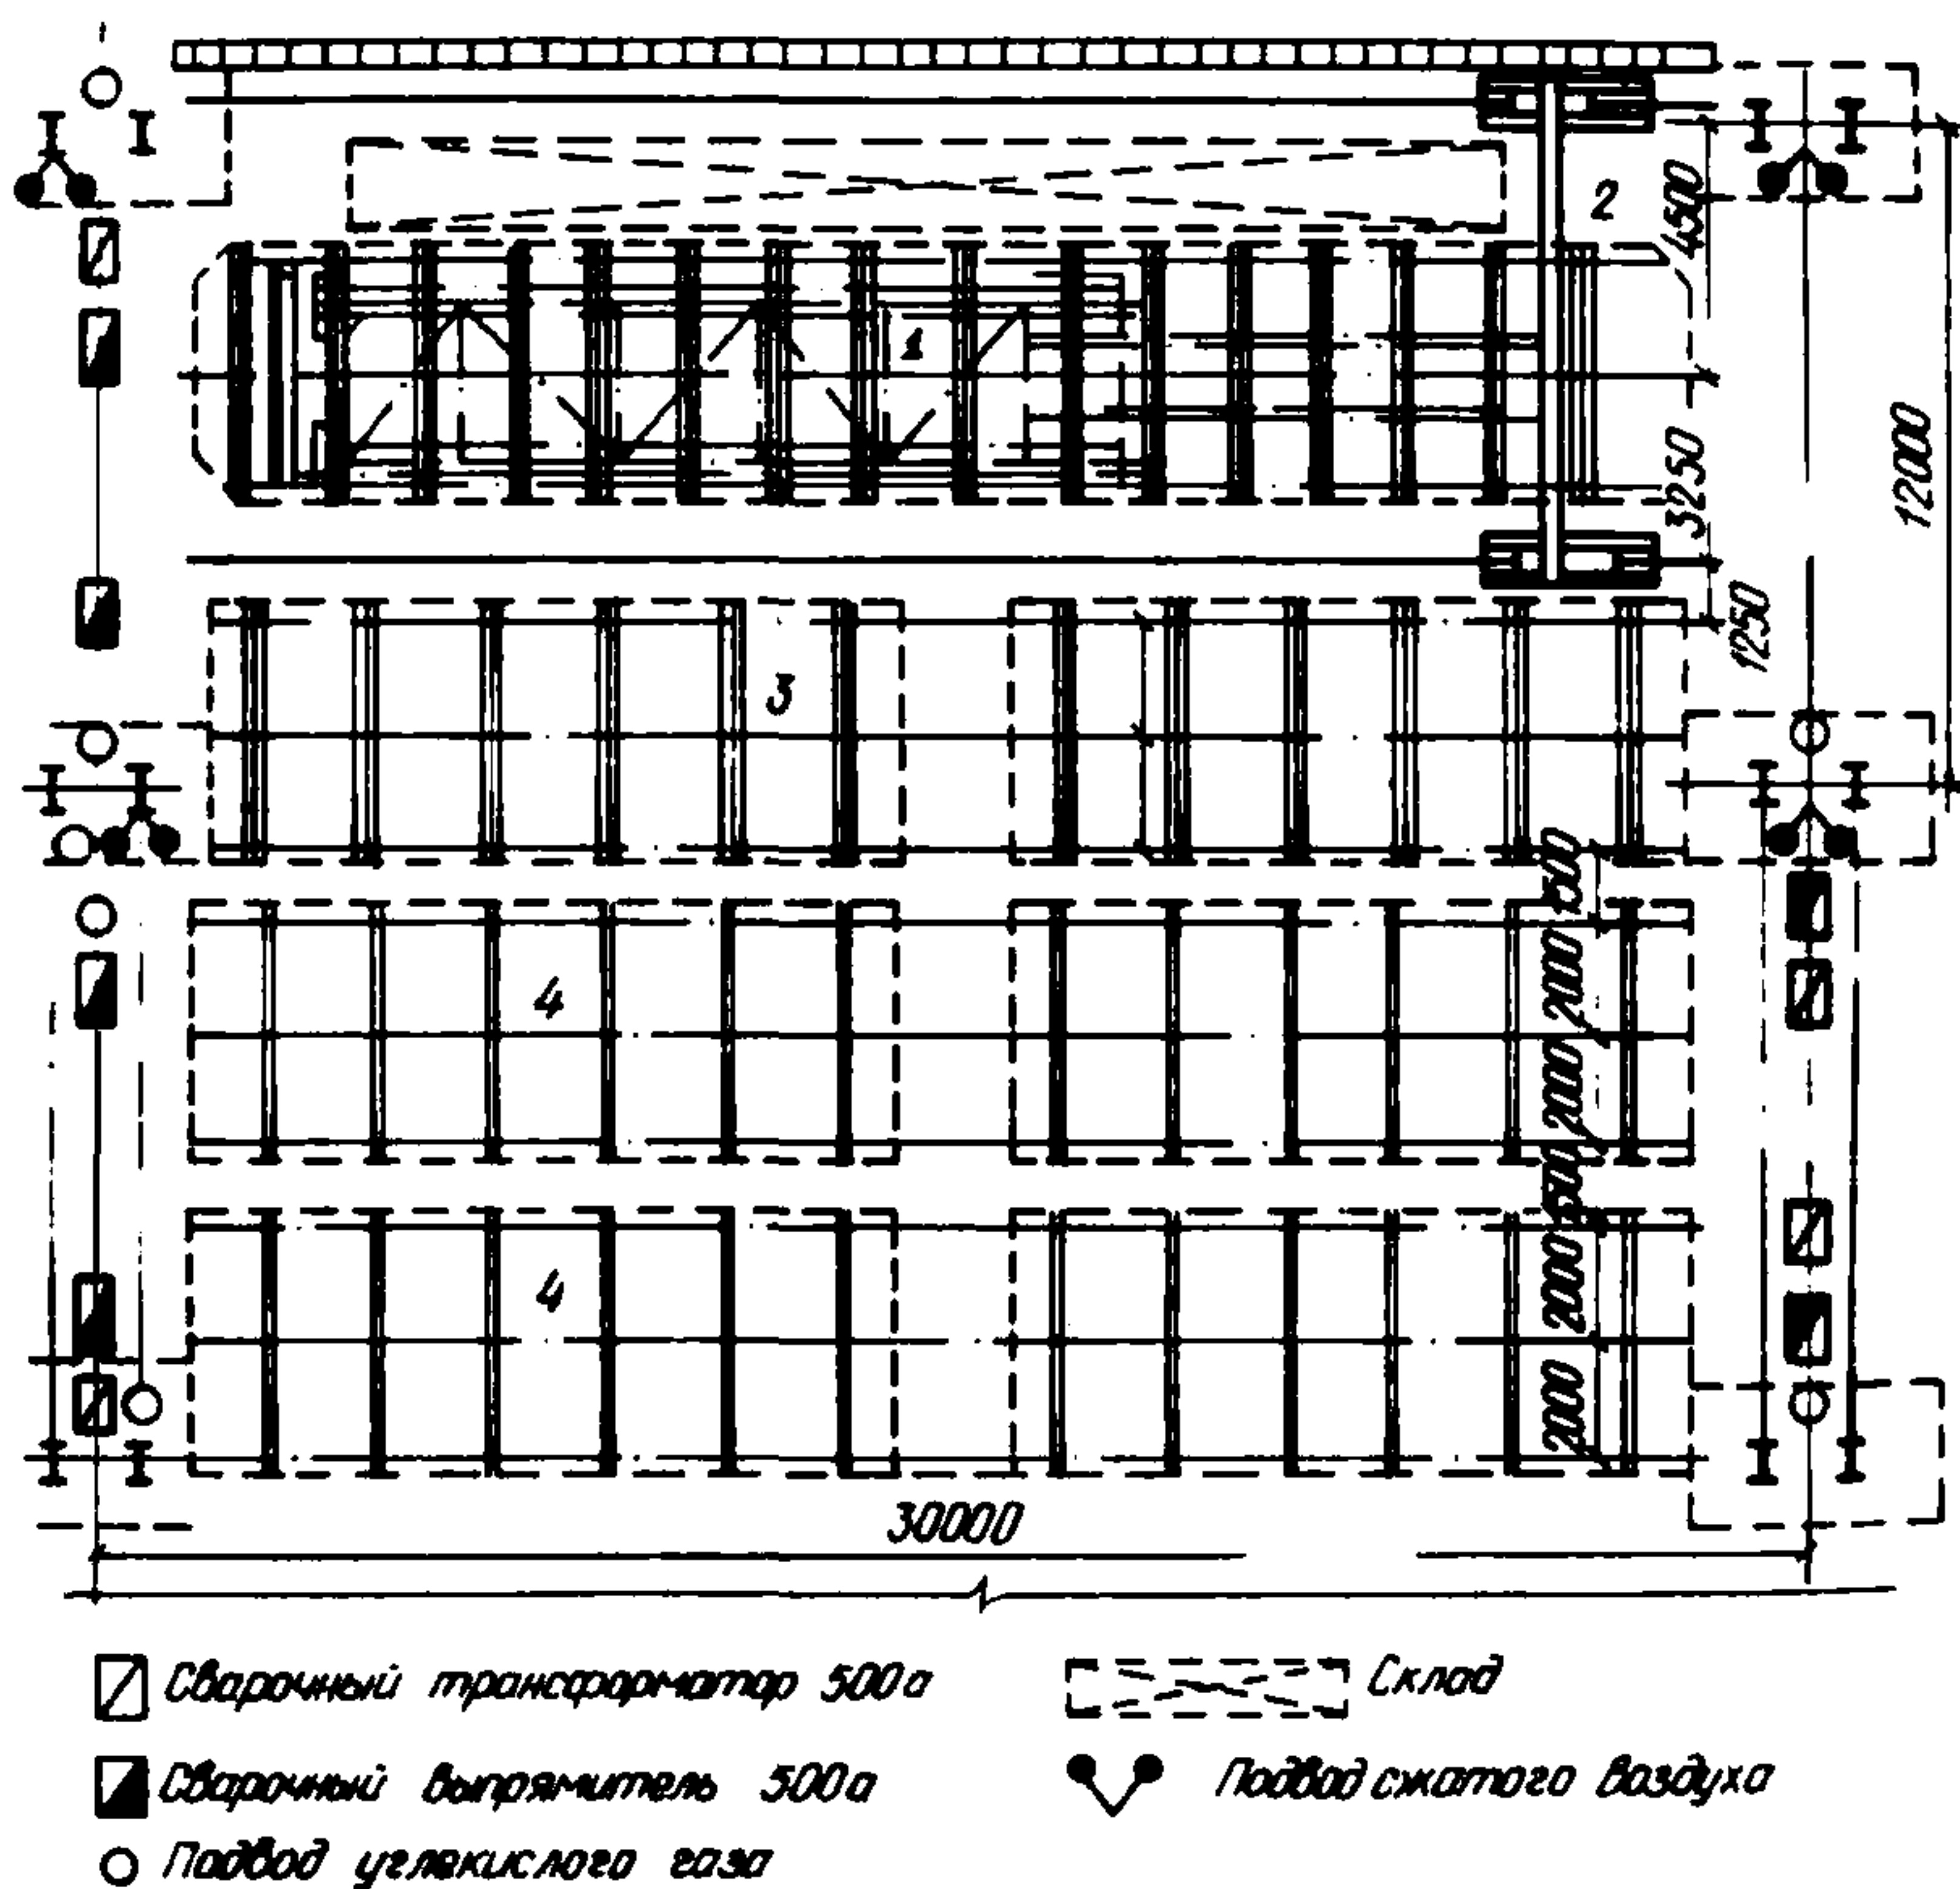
Планировка участка сборки и сварки колонн
